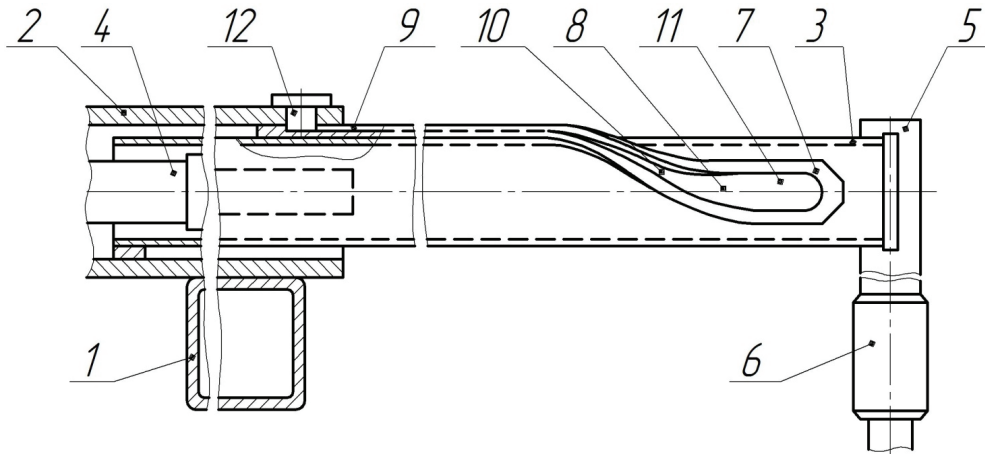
Выдвижная опора с механизмом поворота короткоходового гидродомкрата: 1 – рама; 2 – направляющая; 3 – выдвижная балка; 4 – гидроцилиндр; 5 – кронштейн; 6 – опорный гидродомкрат; 7 – направляющая дорожка; 8 – канавка; 9 – продольная проточка; 10 – винтовая проточка; 11 – продольная проточка; 12 – фиксатор.
